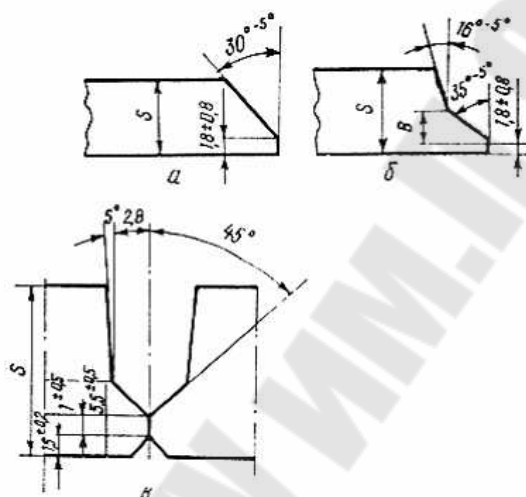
Типы разделки кромок труб для ручной дуговой сварки, односторонней автоматической сварки под флюсом, автоматической дуговой сварки порошковой проволокой с принудительным формированием, полуавтоматической сварки в защитных газах:
